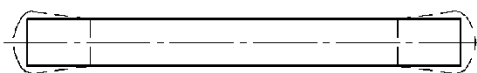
Уширение при прокатке полосовой заготовки переменной толщины
